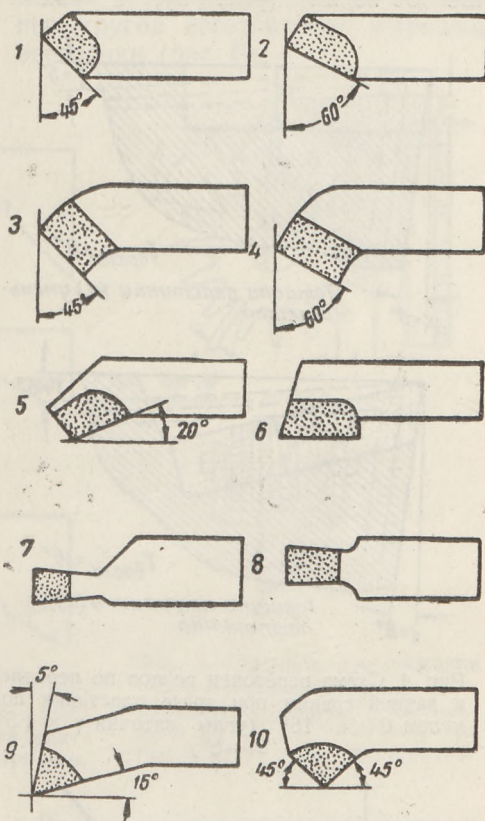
Типы токарных резцов: 1 и 2 — проходной; 3 и 4 — проходной отогнутый; 5 — подрезной торцевой; 6 — подрезной упорный; 7 — отрезной; 8 — прорезной; 9 — расточный для глухих отверстий; 10 — расточный для сквозных отверстий
